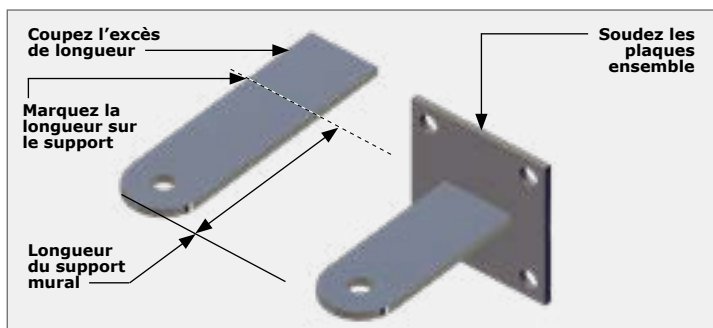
COUPEZ ET SOUDEZ LE SUPPORT
